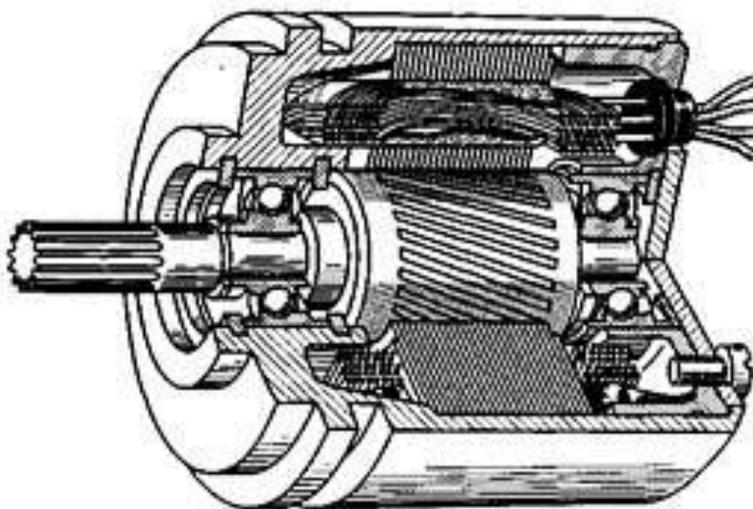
Асинхронный исполнительный двигатель сквозной конструкции
